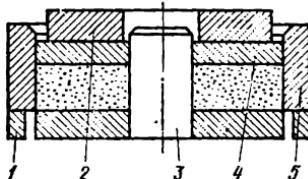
Схема пресс-формы для прессования кругов прямого профиля:
